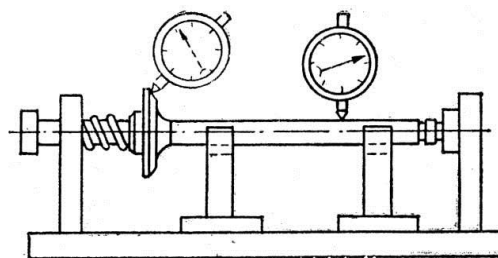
Схема перевірки биття стержня і робочої фаски клапана, встановленого на призмах.
